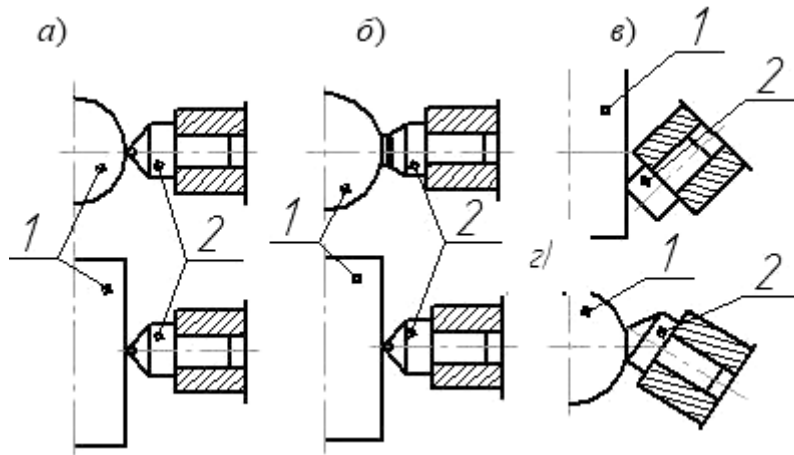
Схема установок выглаживателей при обработке цилиндрической поверхности
